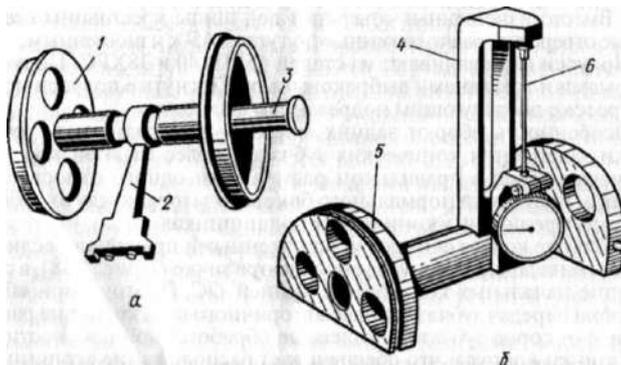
Приспособления для установки вторичного вала (а) коробки передач трактора ДТ-75М и ведущей шестерни главной передачи (б) заднего моста трактора Т-150К:
